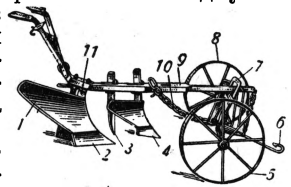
Конный передковый плуг с предплужником: 1—отвал, 2—лемех, 3—нож (черенковый), 4—предплужник, 5—бороздвое колесо, 6—упряжная тяга, 7—вертикальная рама передка, 8—пошное колесо, 9—грядиль, 10—цепь передка, 11—стойка литая.
